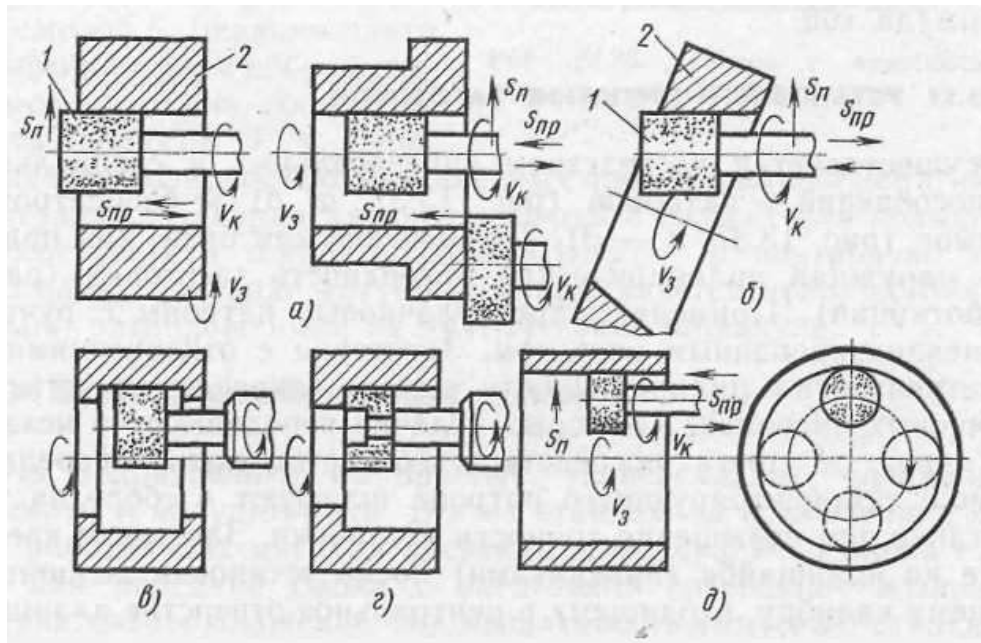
Схеми внутрішнього круглого шліфування: з поздовжньою подачею (а, б); з поперечною подачею (в, г); з планетарним ходом шліфувального круга (д)
